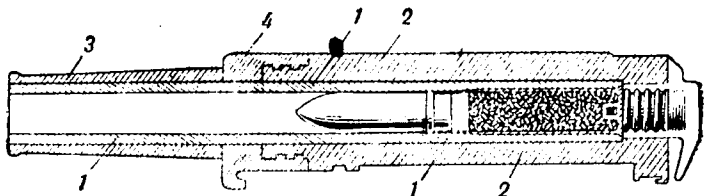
Скрепление нашего 76-миллиметрового полкового орудия кожухом. 1 — труба; 2 — кожух; 3 — надульник; 4 — крепляющее кольцо.
